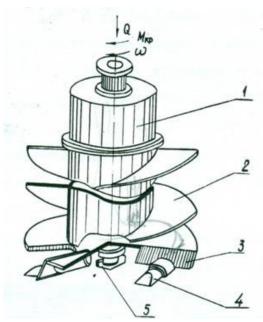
Конструктивная схема бурового рабочего органа: 1 – корпус; 2 – накопитель грунта; 3 – лемех; 4 – ударный инструмент; 5 – забурник.
